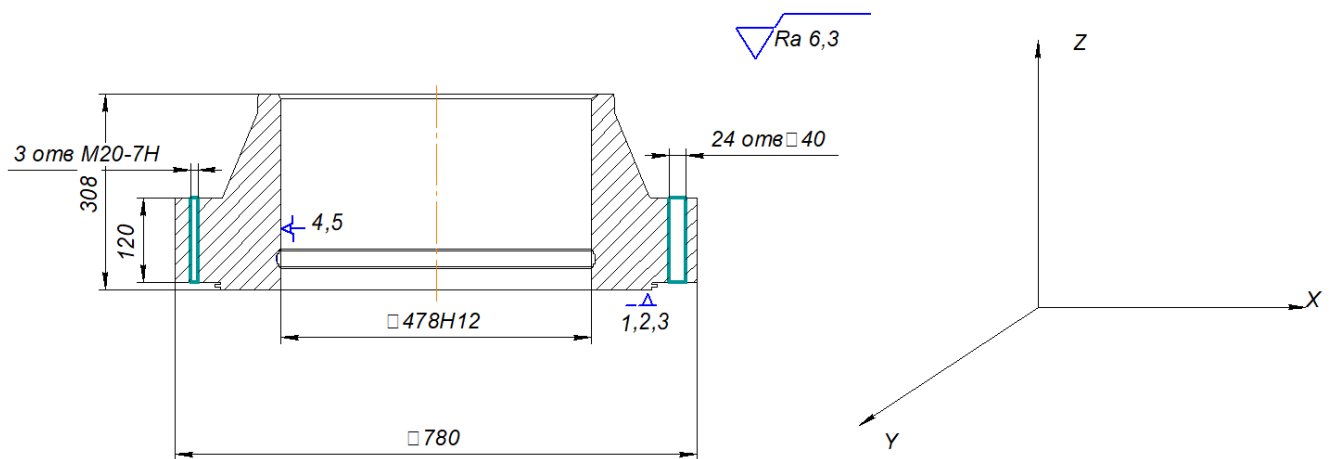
Схема базування заготовки на операції 055 “Фрезерна з ЧПК”
